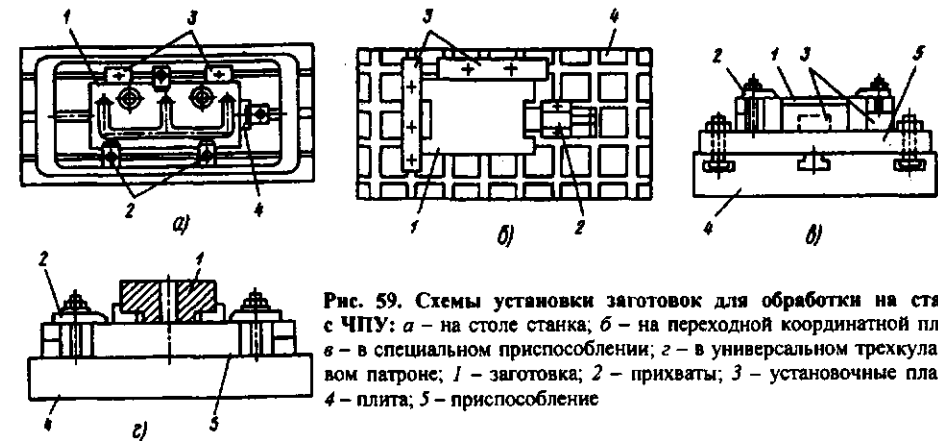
Схемы установки заготовок для обработки на станке с ЧПУ: а – на столе станка; б – на переходной координатной плите; в – в специальном приспособлении; 2 – в универсальном трехкулачковом патроне; 1 – заготовка; 2 – прихваты; 3 – установочные планки; 4 – плита; 5 – приспособление
